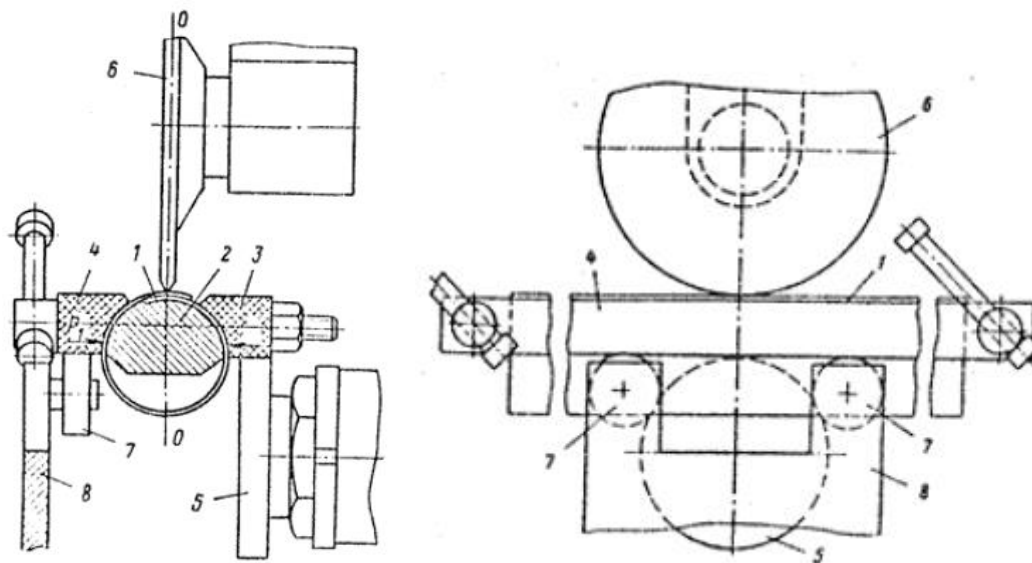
Способ контактной шовной сварки трубчатых деталей
